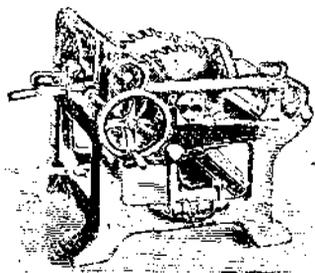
Обрезной станок с двумя круглыми пилами и цепной подачей.
